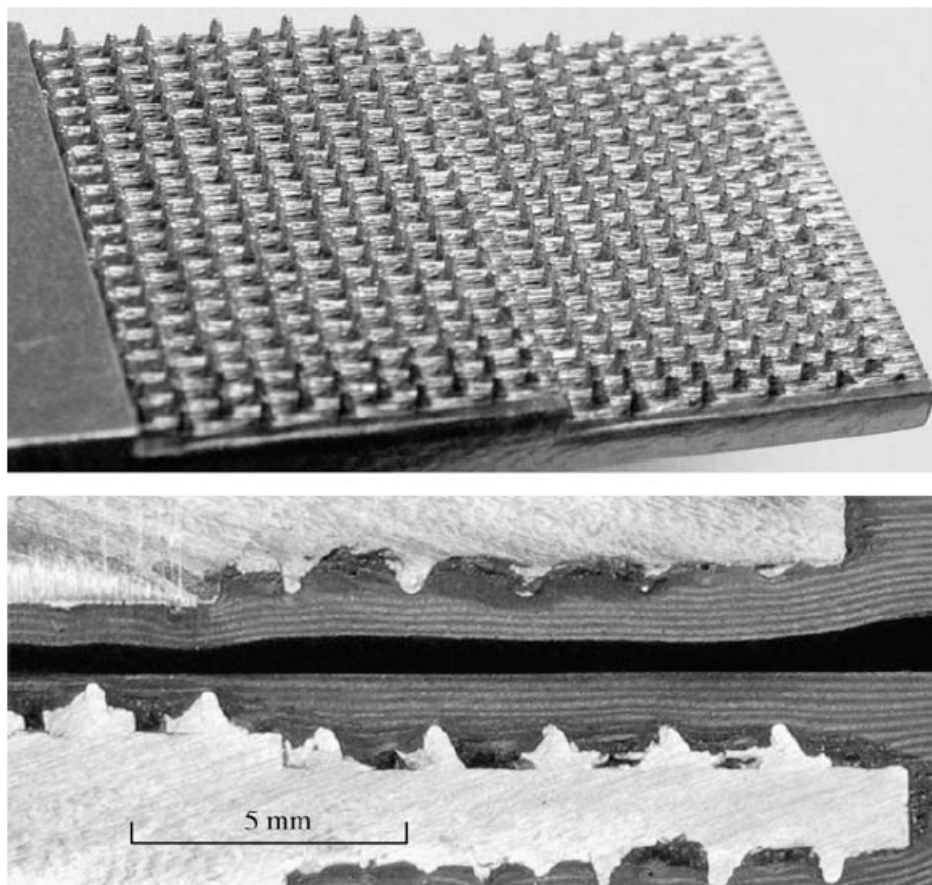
Vue macroscopique de la surface texturée par la technologie Surfisculpt et joint COMELDTM métal-fibre de verre
